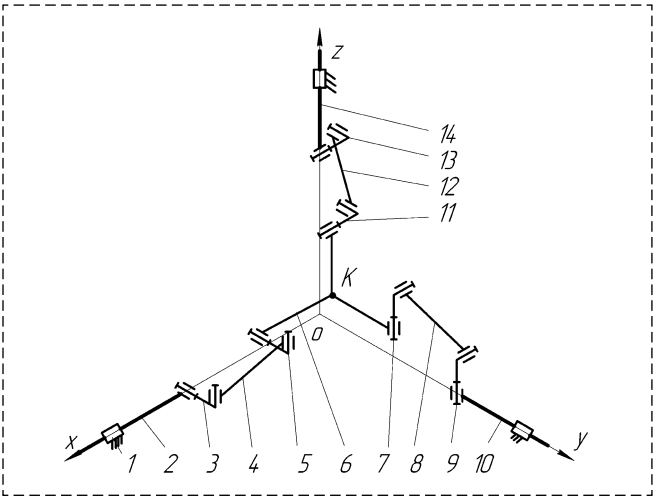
Самоустанавливающийся механизм с карданными шарнирами
